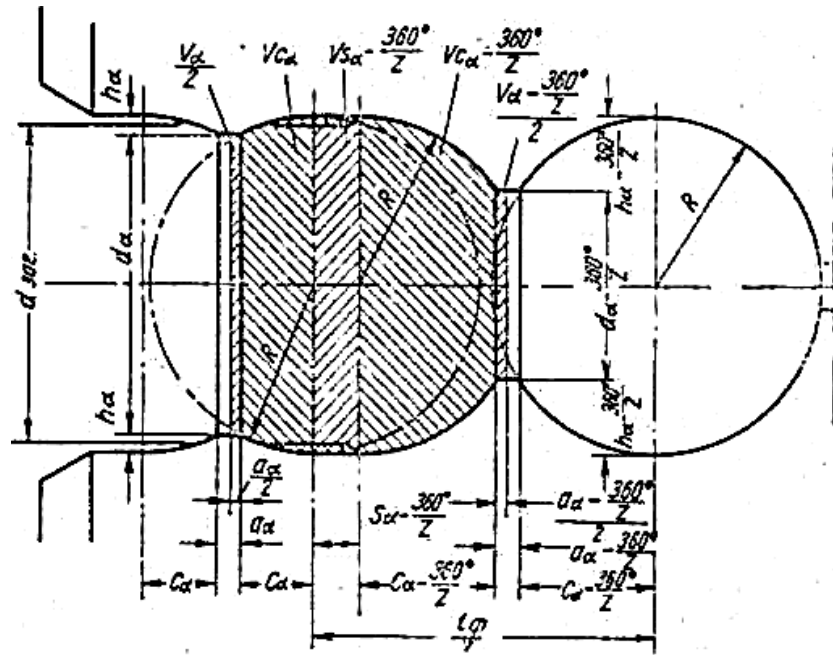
Расчет калибра в момент захвата заготовки
